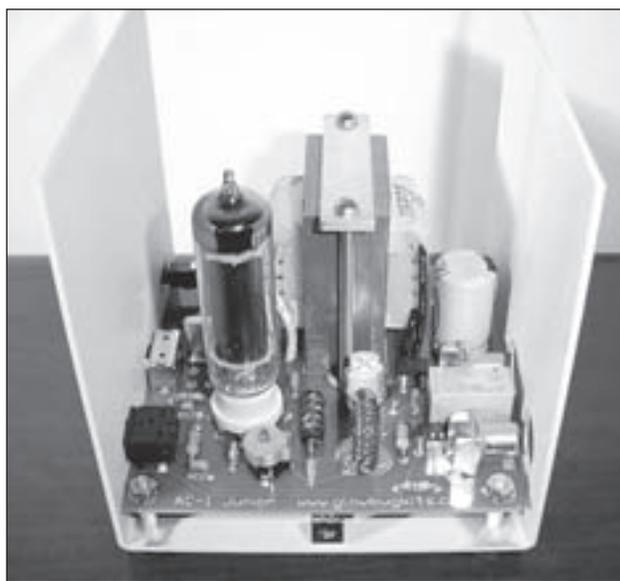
Foto E. Vista del interior del Glowbug. Observa el único toroide cerca del panel frontal y el transformador de alimentación montado de lado para que encaje mejor.
